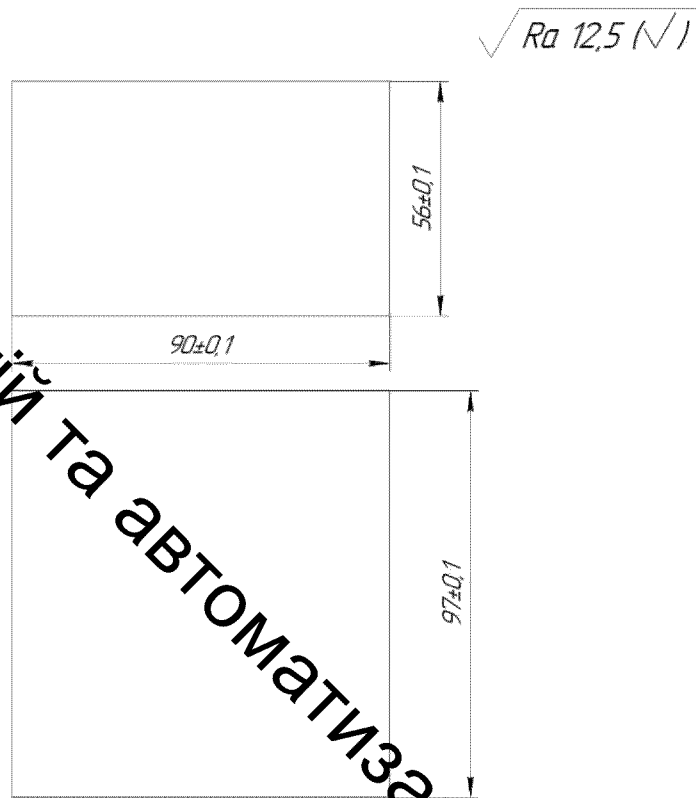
Ескіз заготовки, отриманої з прокату сортового сталевих
